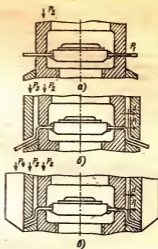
Конструкция штампа для формовки и обрезки выводов микросхем:
